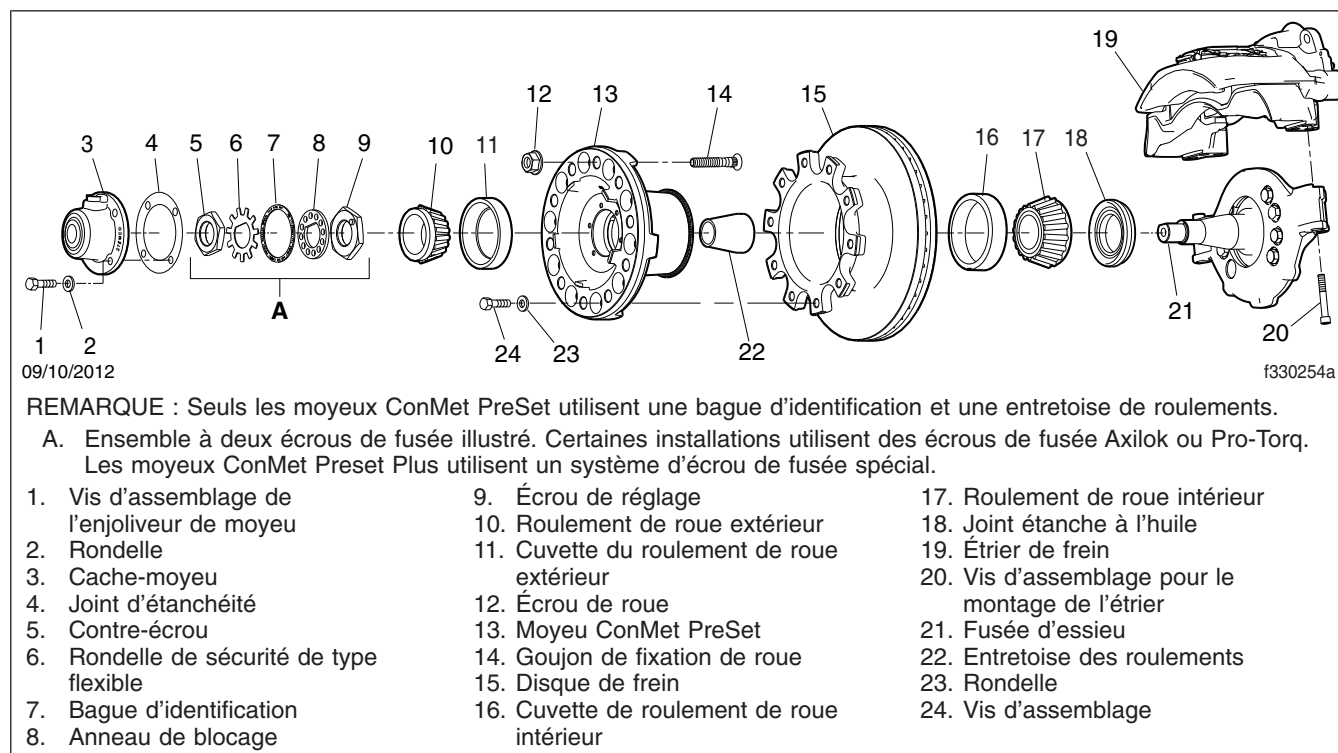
, Ensemble d'extrémité de roue type, essieu avant avec freins à disque
